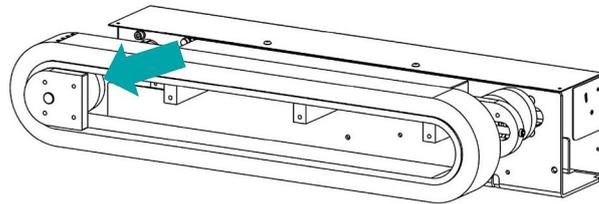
, Antriebsrolle mit Bürstenriemen demontieren
